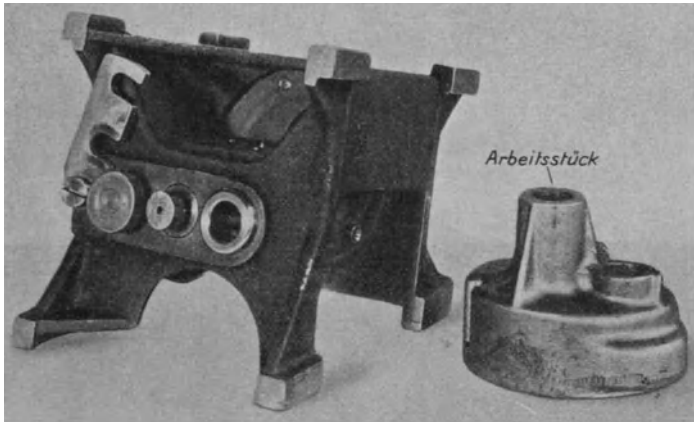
Bohrvorrichtung für den Getriebekasten zur elektrischen Bohrmaschine.
